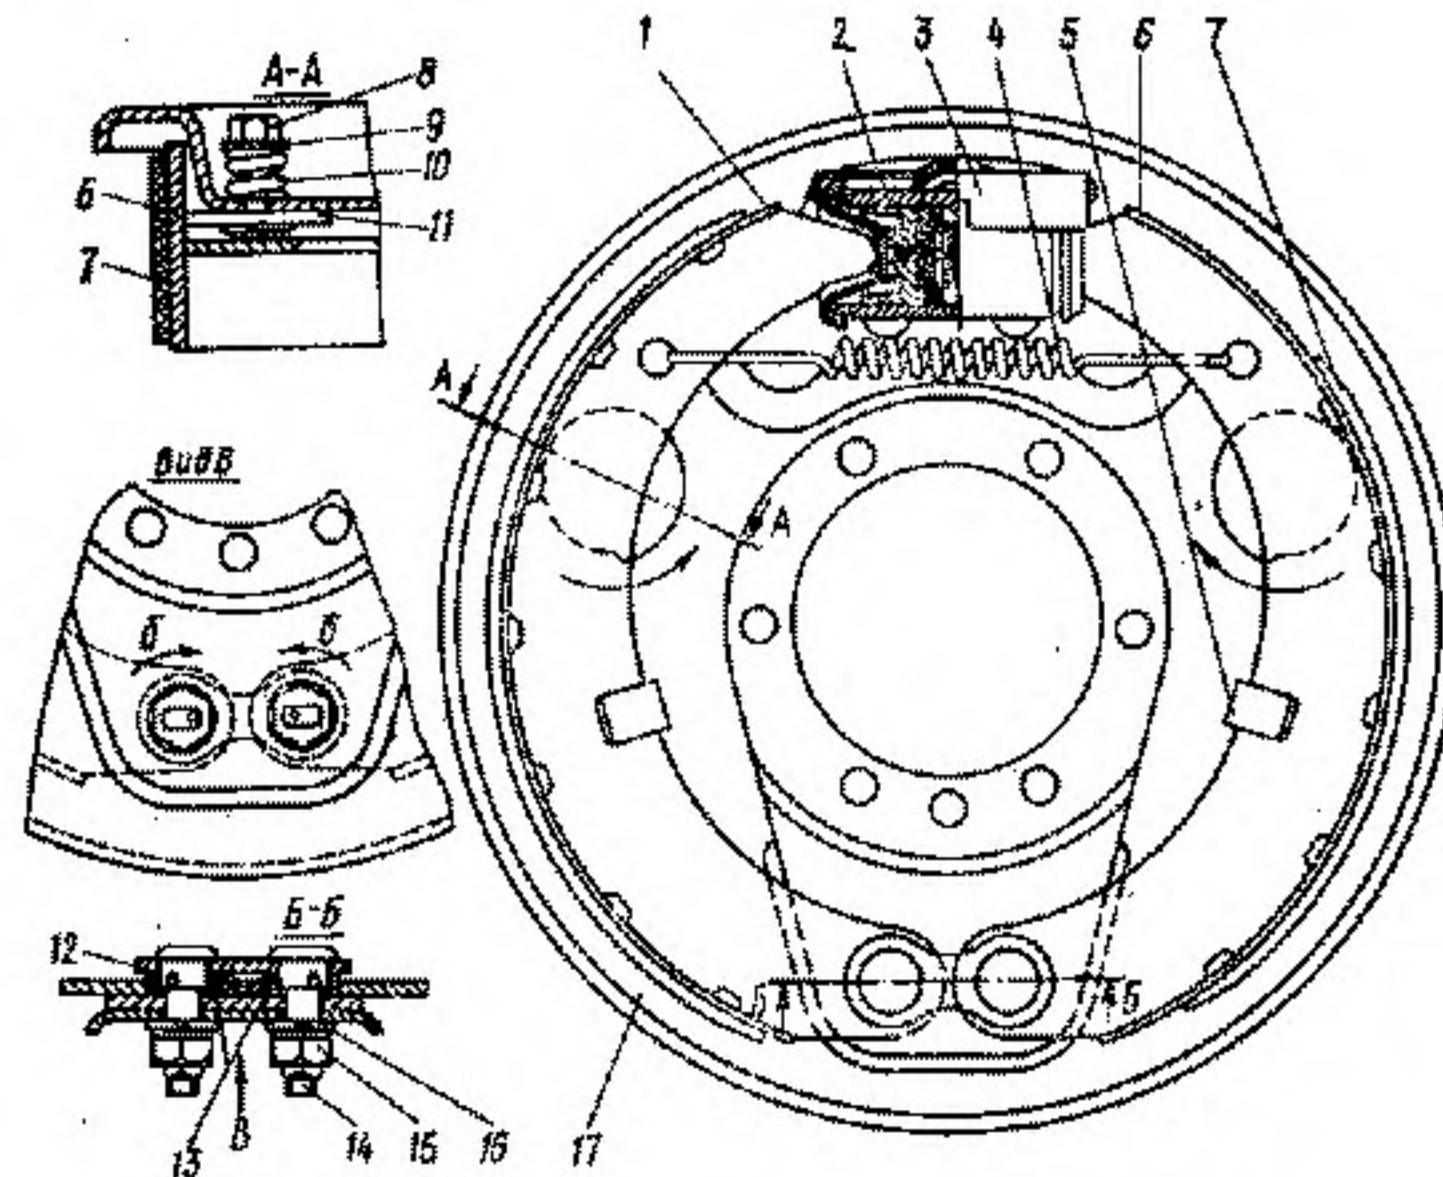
Рабочий тормоз автомобиля ГАЗ-53-12:
